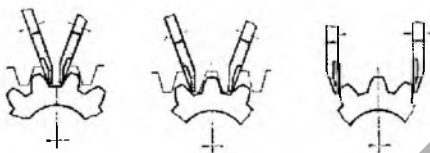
Схема шлифования зубчатых колес тарельчатыми кругами и схемы их установки
